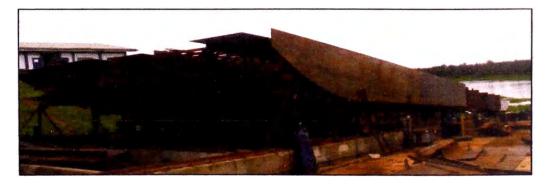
Instalación de Plancha de Banda Br-Proa
